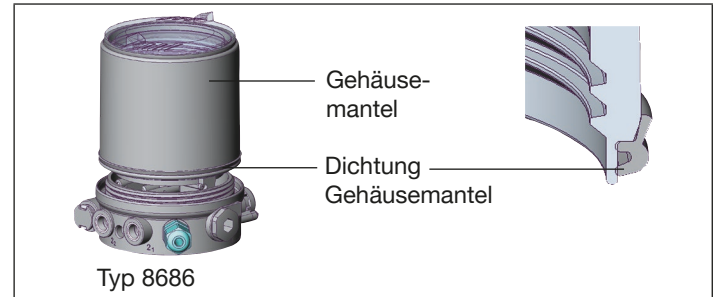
Position Dichtung Klarsichthaube / Gehäusemantel
